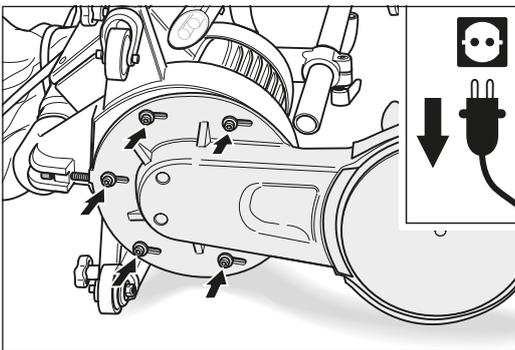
de que se enrosque en de 3 a 4 vueltas el tornillo tensor de la correa y se vuelva a apretar el brazo antepuesto.
